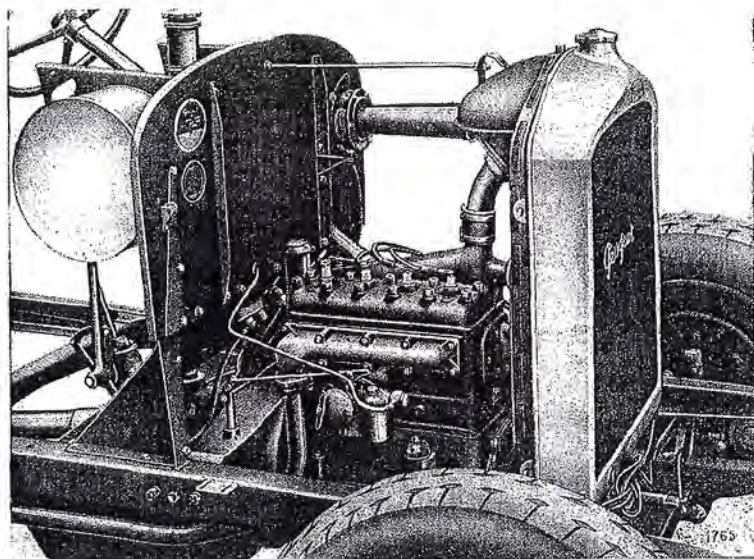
MOTEUR COTÉ CARBURATEUR
